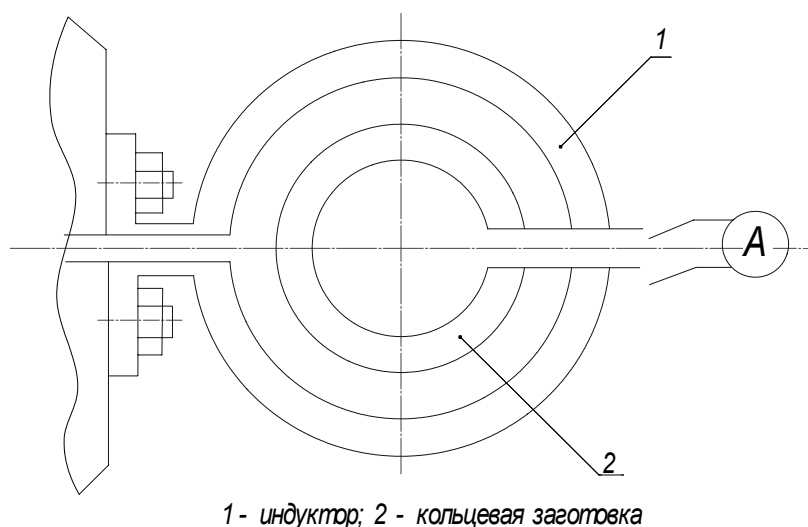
Схема нагрева детали индуктивными токами
